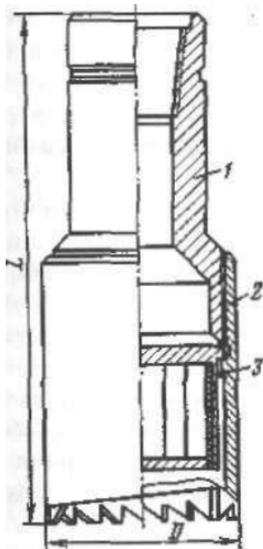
Магнитный фрезер-ловитель типа ФМ:
